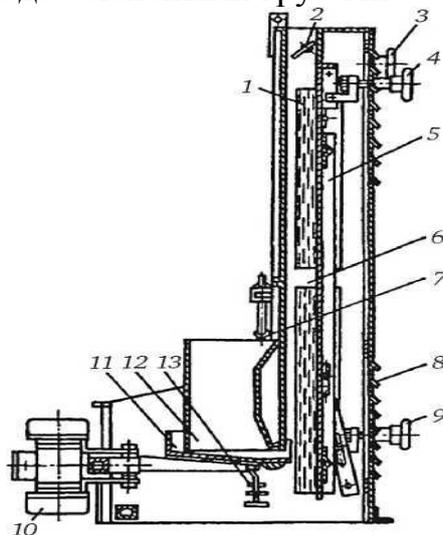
Воздушный сепаратор РЗ-БАБ: 1 - смотровое окно; 2 - дроссельная заслонка; 3 - штурвал заслонки; 4,9 - штурвалы подвижной стенки; 5 - подвижная стенка; 6 - пневмосепарирующий канал; 7 - пружина; 8 - жалюзи; 10 - вибратор 11 - вибрлоток; 12 - приемная камера; 13 - ограничитель хода
